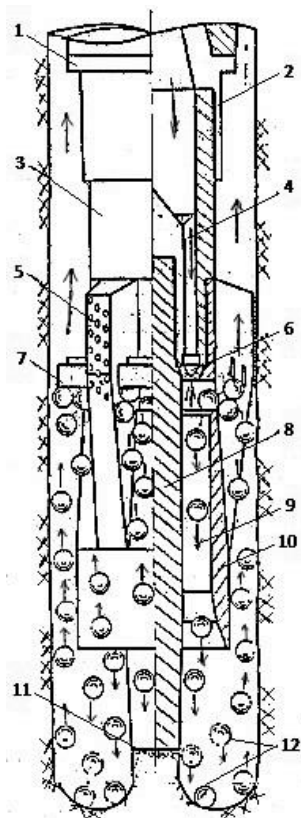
Шароструйно-эжекторный буровой снаряд с соплом и камерой смешения кольцевой формы:
